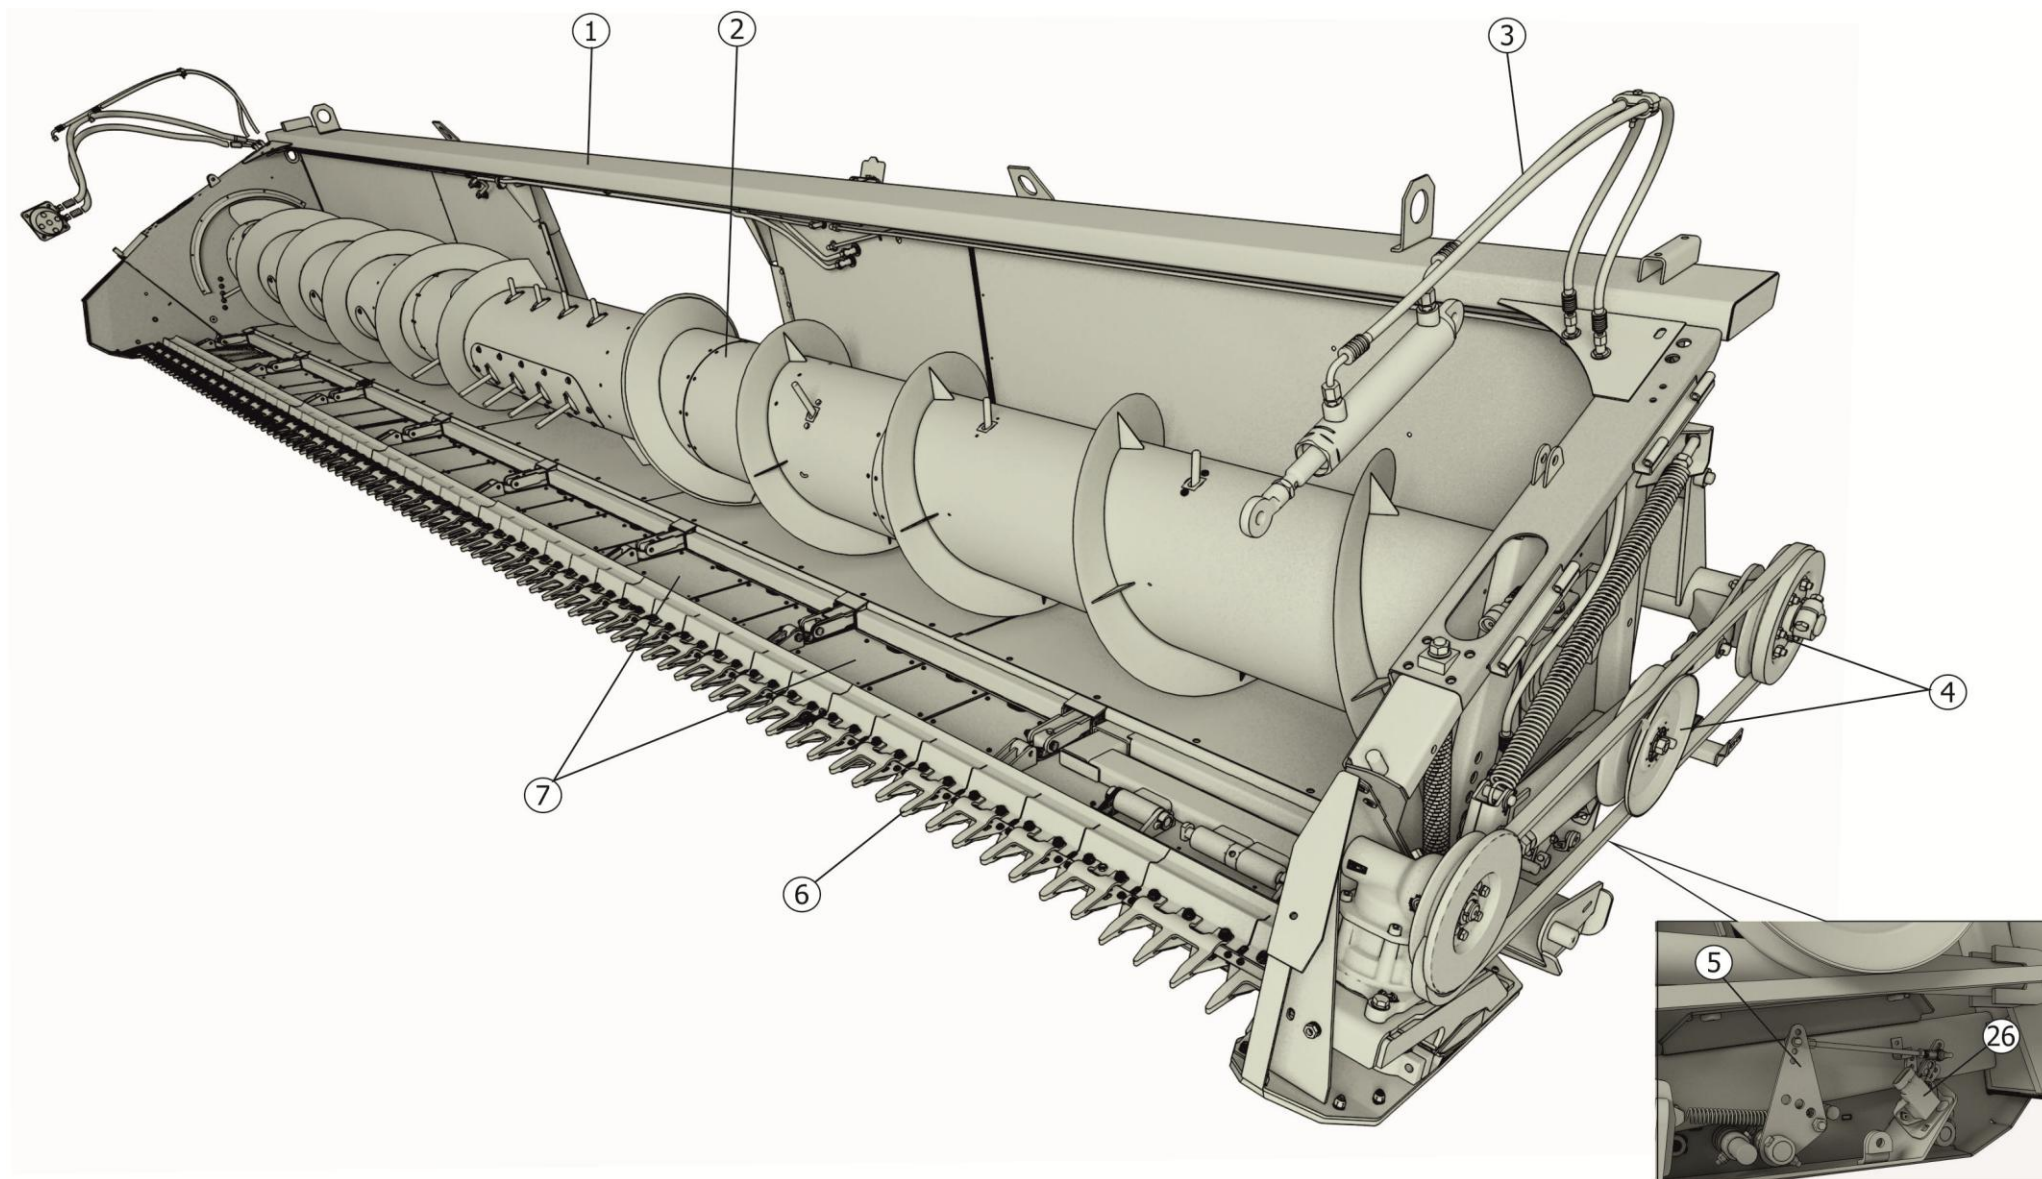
Корпус ЖСУ-703.01.00.000
